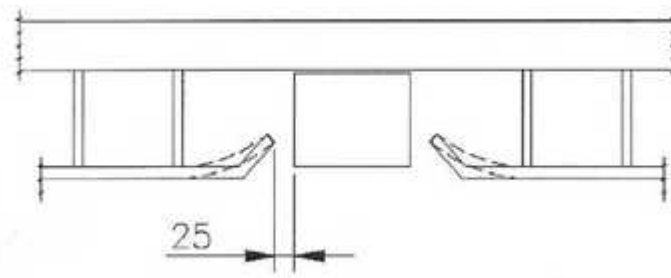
, Holgura con componentes del vehículo, Vista Superior (dimensiones en mm)
